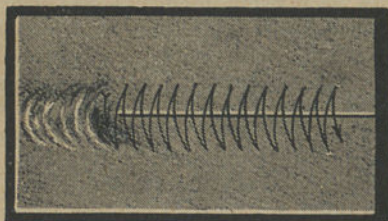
Movimentos do maçarico para a soldadura de chapas de 4 m/m.
